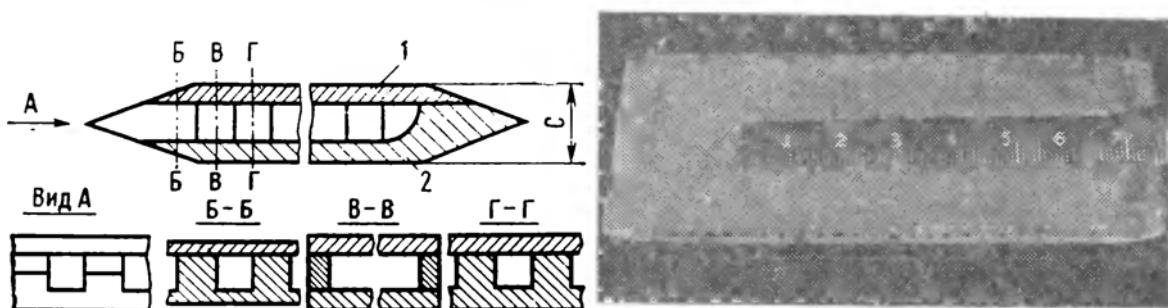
Конструкция охлаждаемых планов и боковин с фрезерованными каналами:
